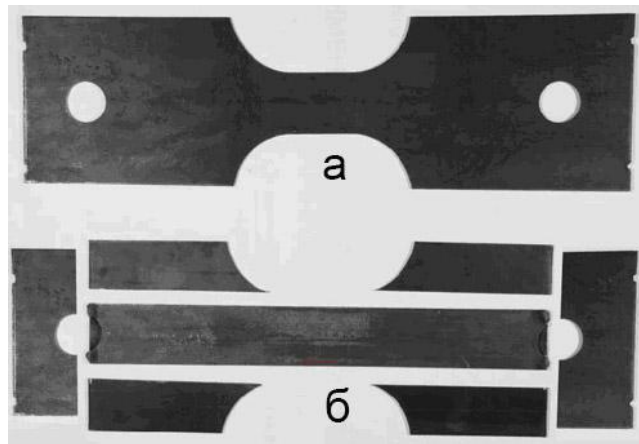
Зразки для пластичного деформування розтягом: а – для деформування, б – для наведення напружень
